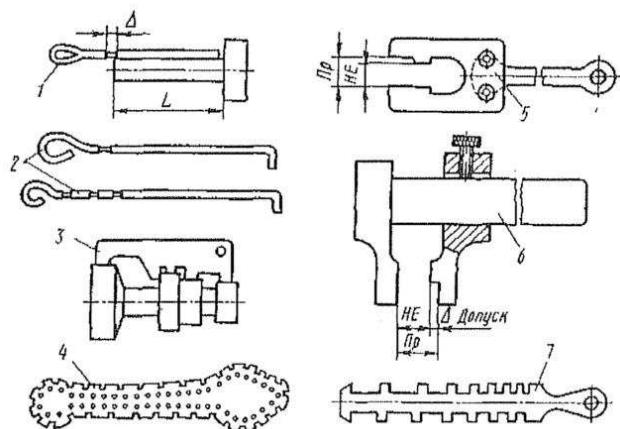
Специальный мерительный инструмент: 1 – усадочный шаблон; 2 – прутковые шаблоны; 3 – профильные шаблоны; 4 – контурные шаблоны; 5 – калибровочная скоба; 6 – регулируемая скоба; 7 – калибр-гребенка
